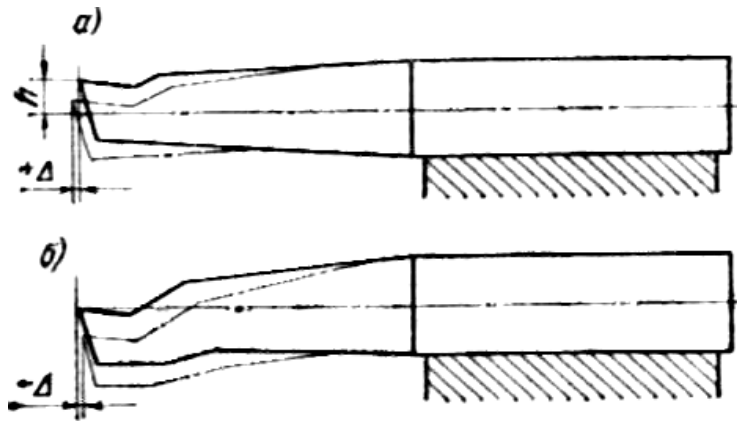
Типи розточувальних різців і схеми деформації їх робочої частини в процесі обробки
